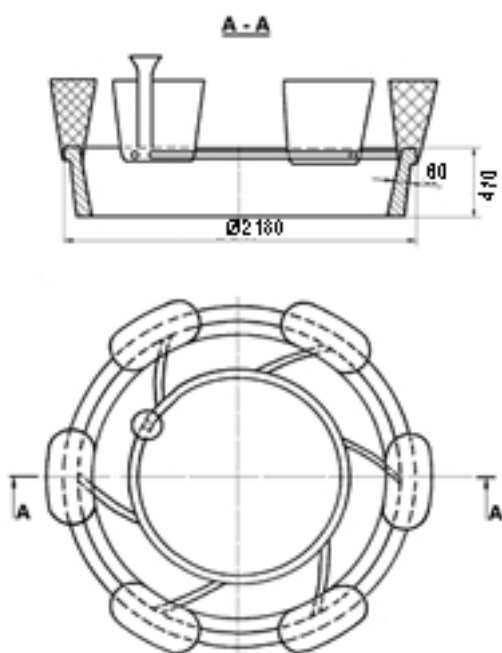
Схема подвода металла в толстостенные части отливки
